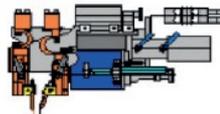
Z und F160-Z - Schweißzangen für die Automatisierung
